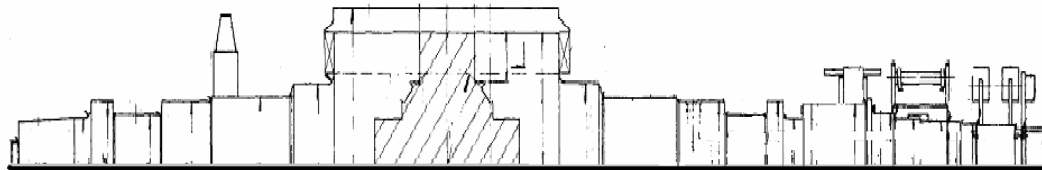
DESENHO DO ROTOR DO MOTOR
